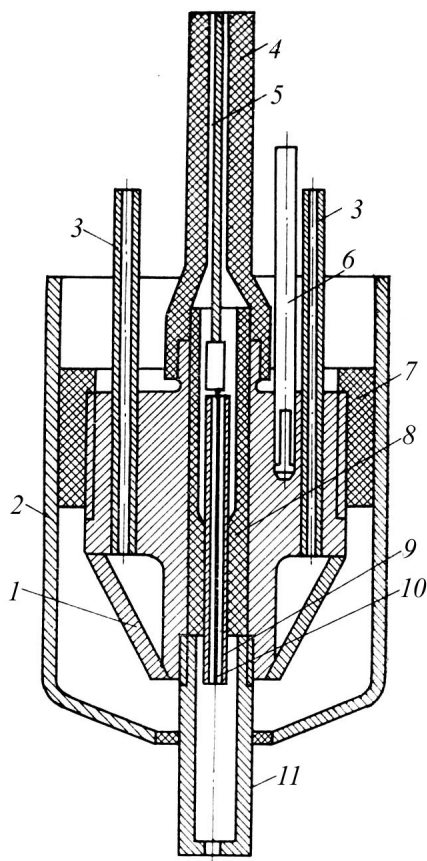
Пальник для дугового зварювання у вакуумі:
